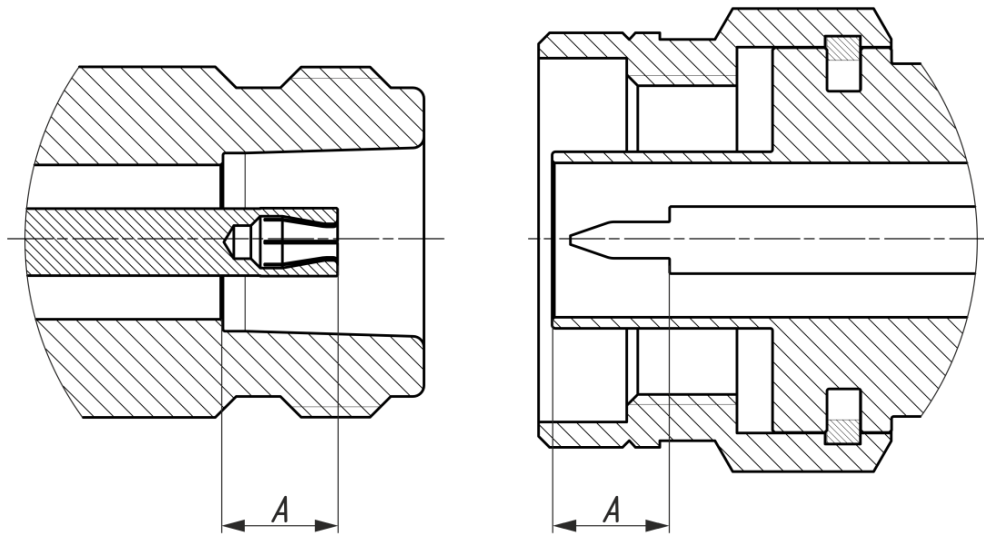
Соединители тип N и III (розетка и вилка)
